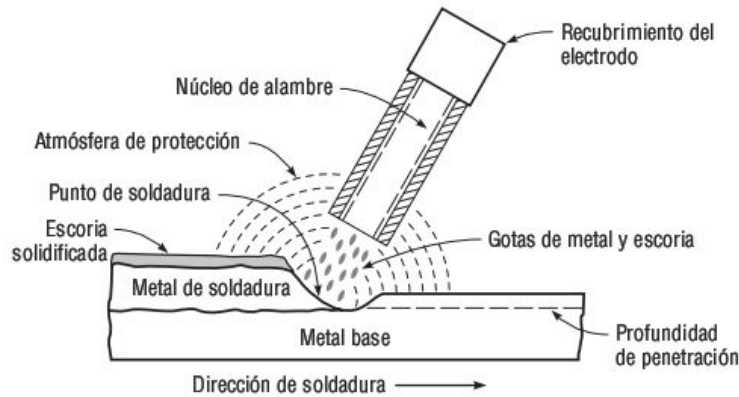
Diagrama esquemático de soldadura con arco.
